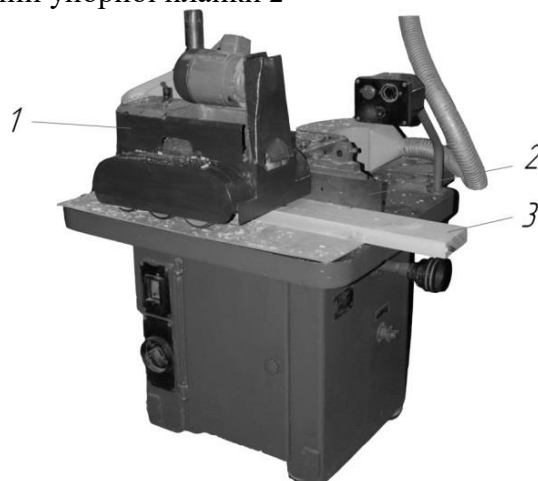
Експериментальна установка на базі фрезувального верстата ФС-1
